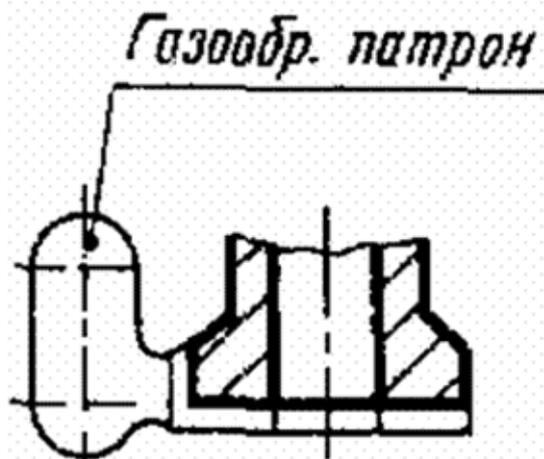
Изображение мест установки газообразующих патронов на чертеже отливки
